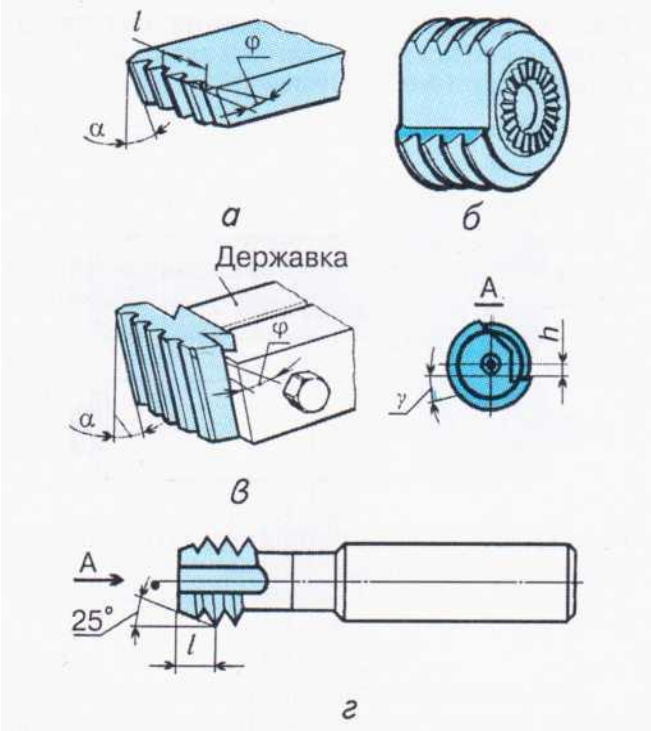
НАРІЗНІ РІЗЦІ, ЩО ПЕРЕТОЧУЮТЬ ПО ПЕРЕДНІЙ ПОВЕРХНІ:
